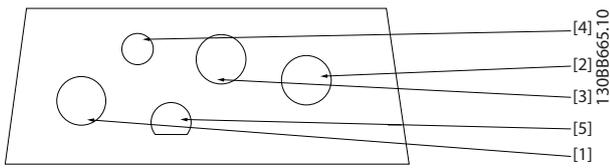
A4 - Kabeleinführungsöffnungen mit Gewinde IP55
